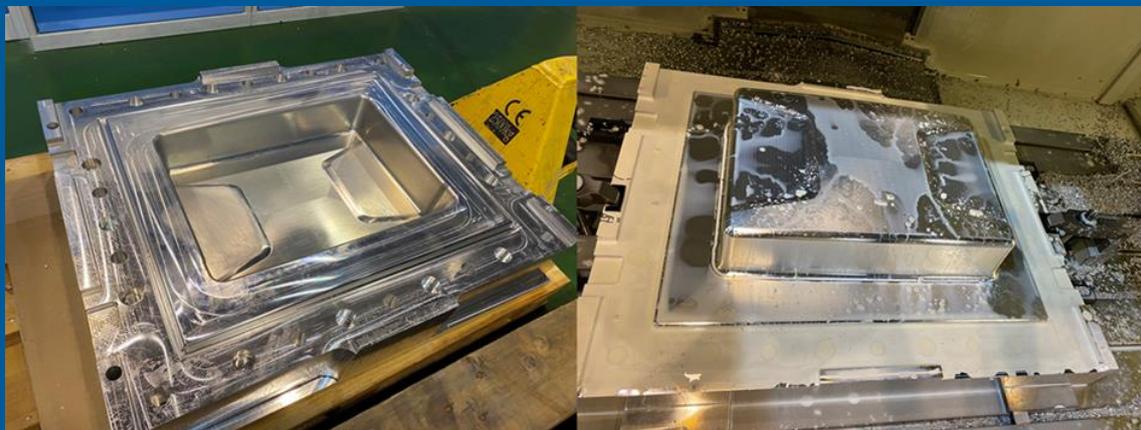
Eines der Werkzeuge für die Thermoformversuche
